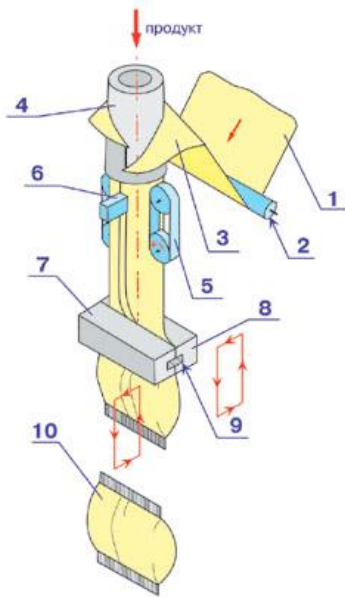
Компонування машини з губками зварювання і протяжки: 1, 3 – плівка; 2 – механізм натягу плівки; 4 – рукавоутворювач; 5 – механізм протягування плівки; 6 – губка поздовжнього зварювання; 7, 8 – губки поперечного зварювання; 9 – відрізний механізм; 10 – готовий пакет
